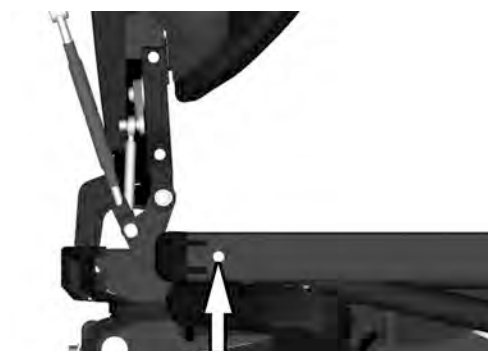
Hintere Befestigungsschraube der UniTrack-Schiene.
